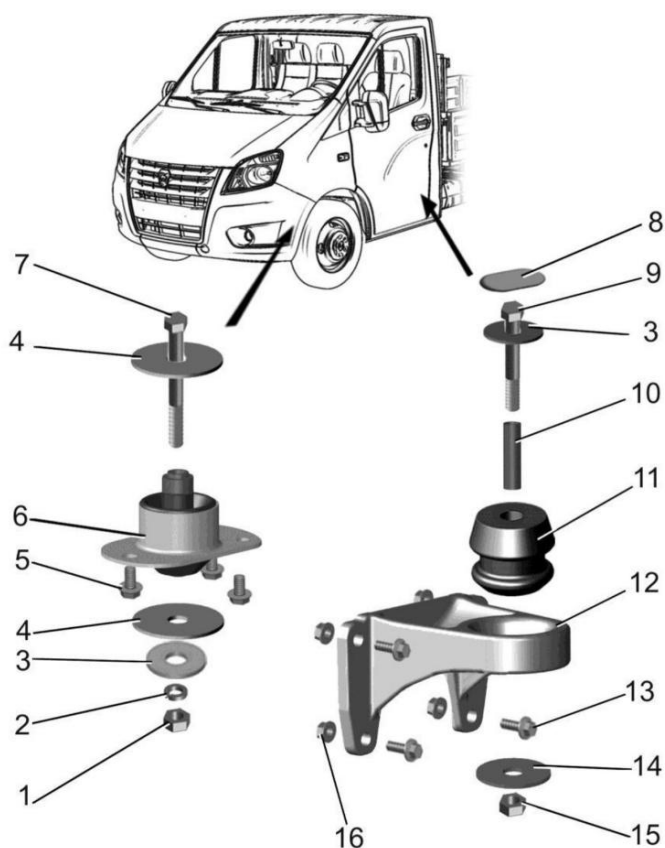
Установка кабины автомобиля ГАЗель NEXT:
